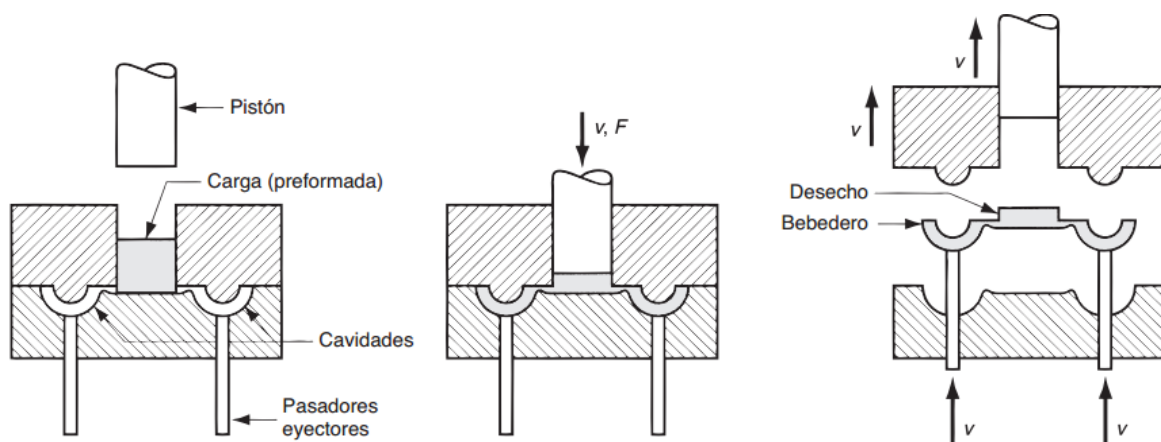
Moldeo por transferencia, un sistema que recoge características del moldeo por compresión e inyección.
